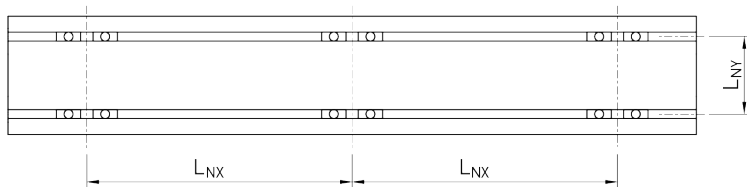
Rozstaw otworów do montażu osi liniowych HT250L od dołu za pomocą bloków ślizgowych
